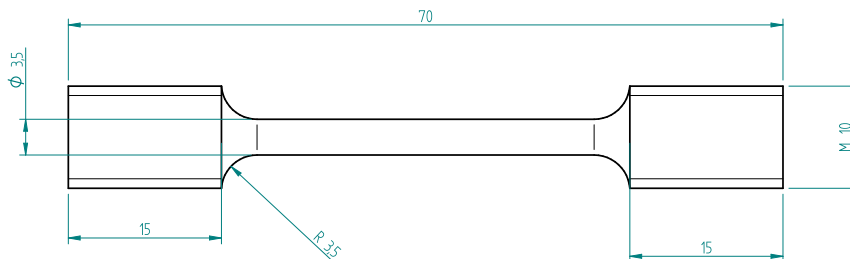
Plan des éprouvettes de traction cylindriques (dimensions en mm)
